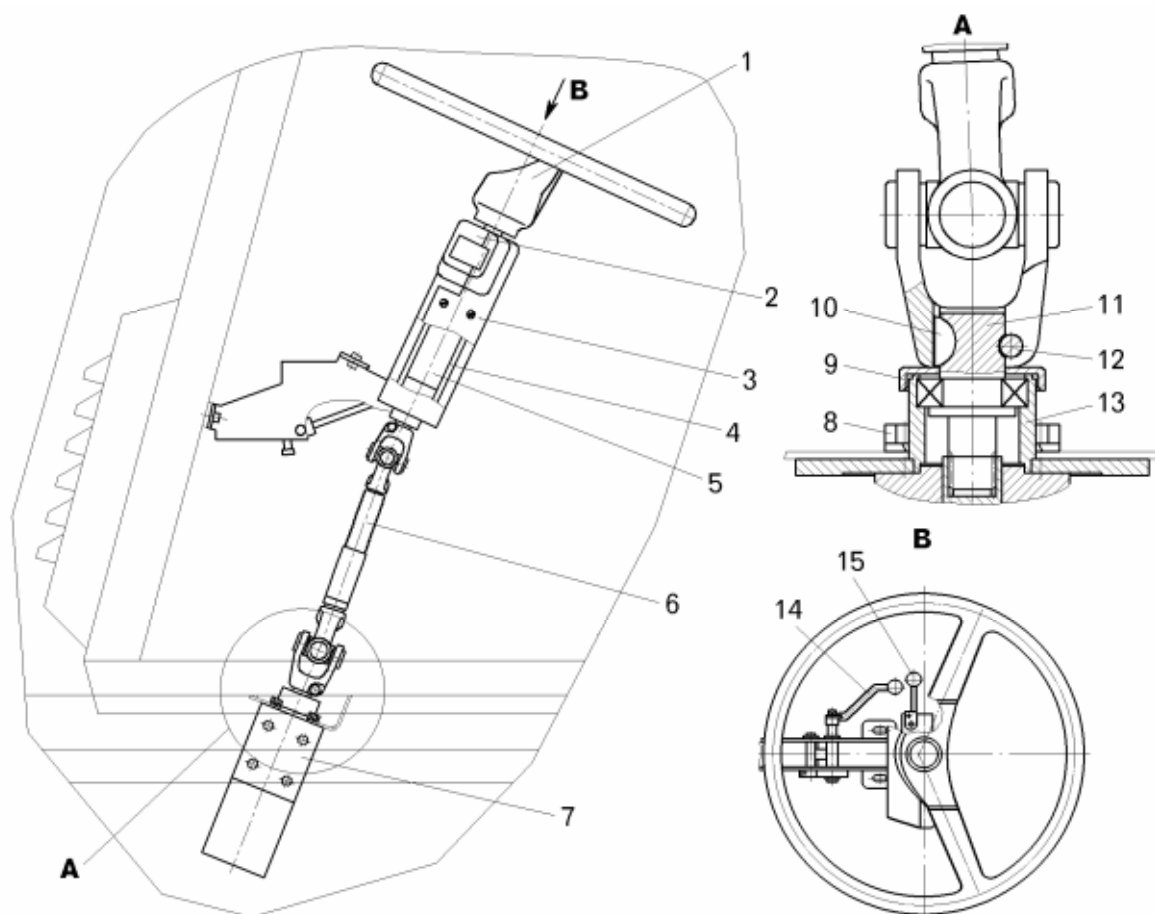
Механический привод гидравлического рулевого механизма:
